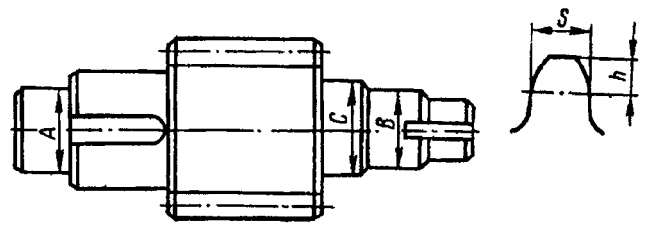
Колесо зубчатое ведущее цилиндрическое
